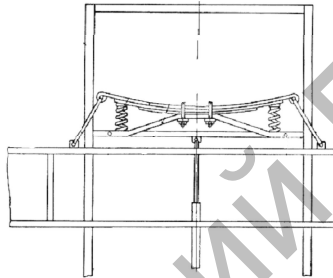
Схема маятниково-рессорной навески с кронштейном штанги опрыскивателя [39]
